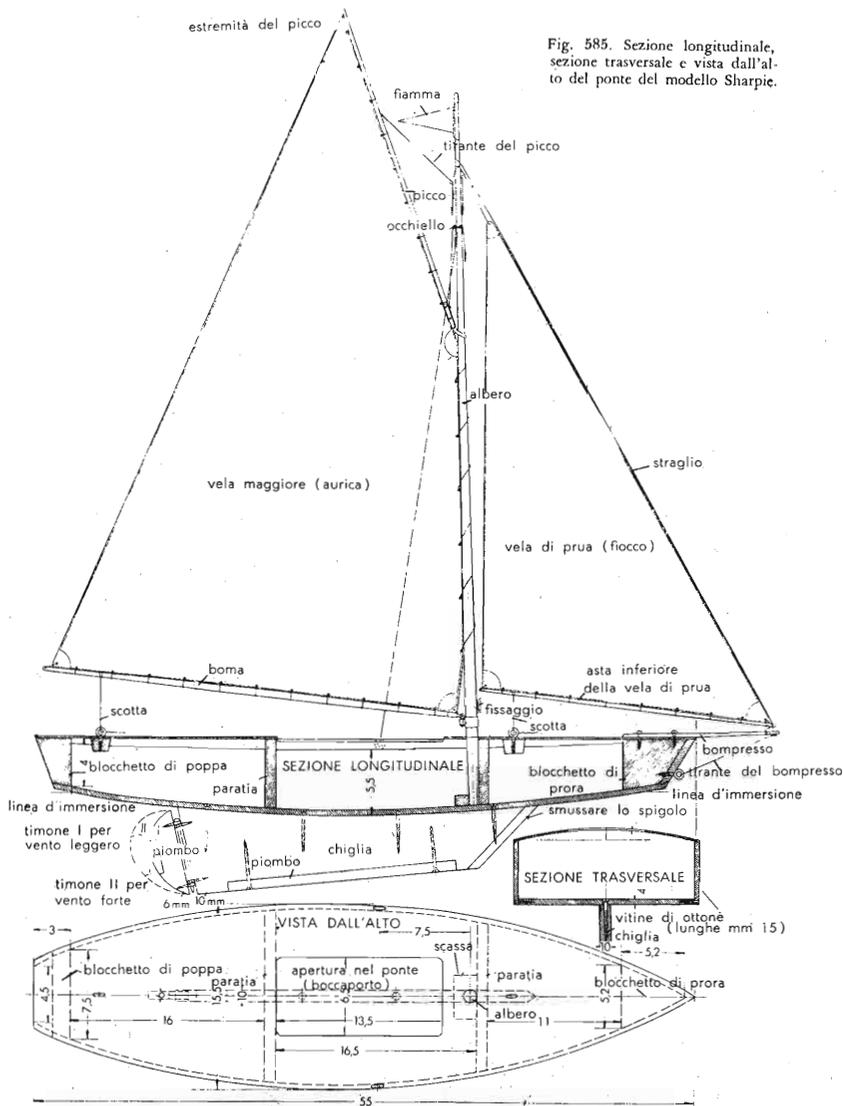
Sezione longitudinale, sezione trasversale e vista dall'alto del ponte del modello Sharpie.
